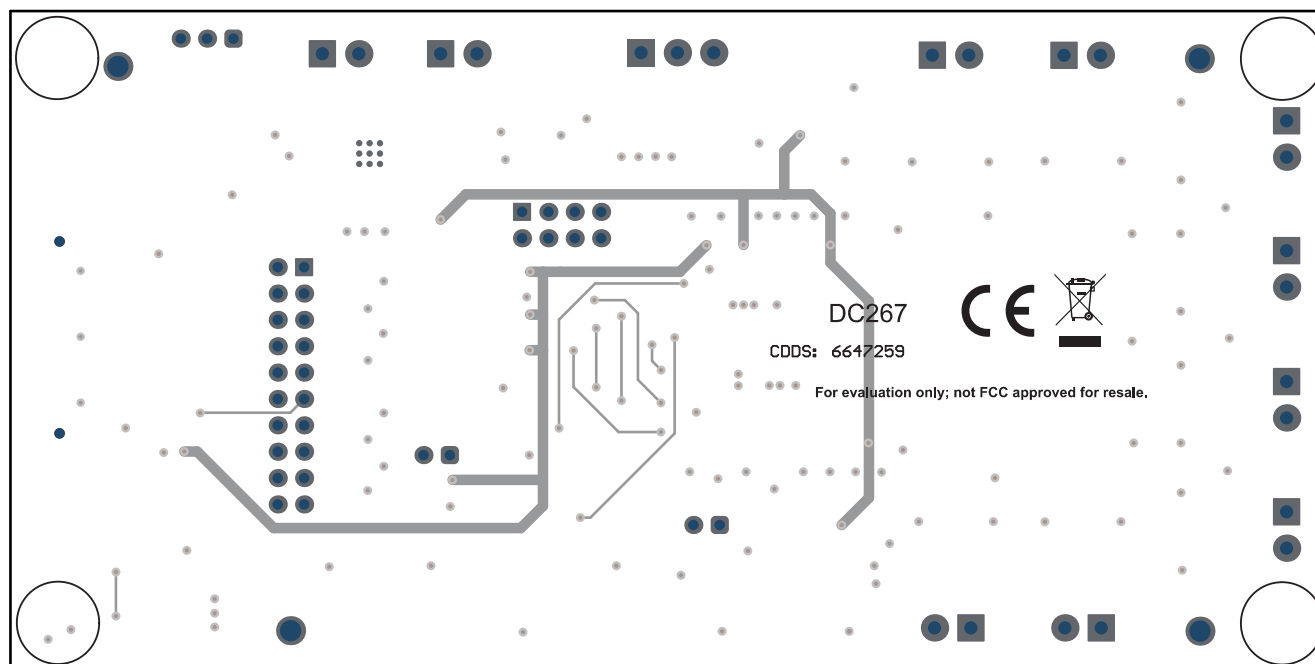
ADS131E08EVM 的 PCB 布局 (底视图)
